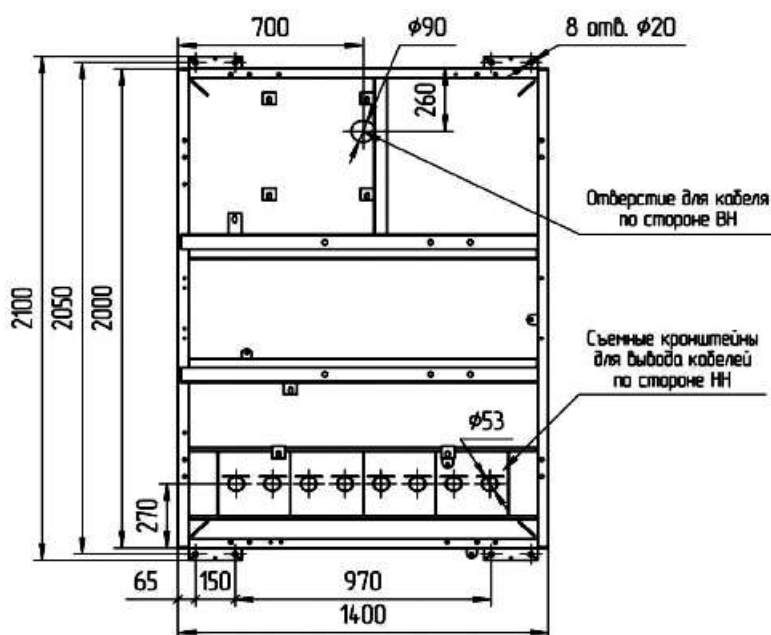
Установочные и присоединительные размеры тупиковой КТПн
